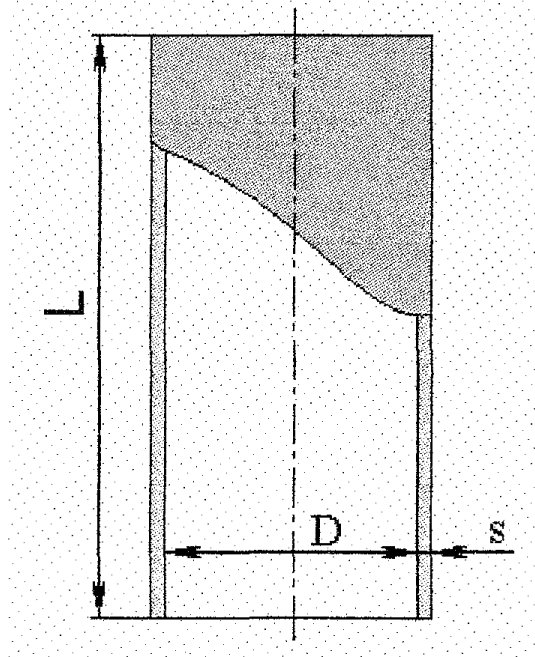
Розрахункова схема обичайки циліндричної
